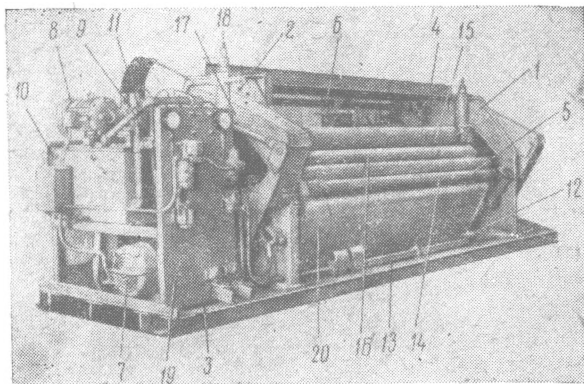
Комбинированная машина для стонки навала и очистки мездры.
